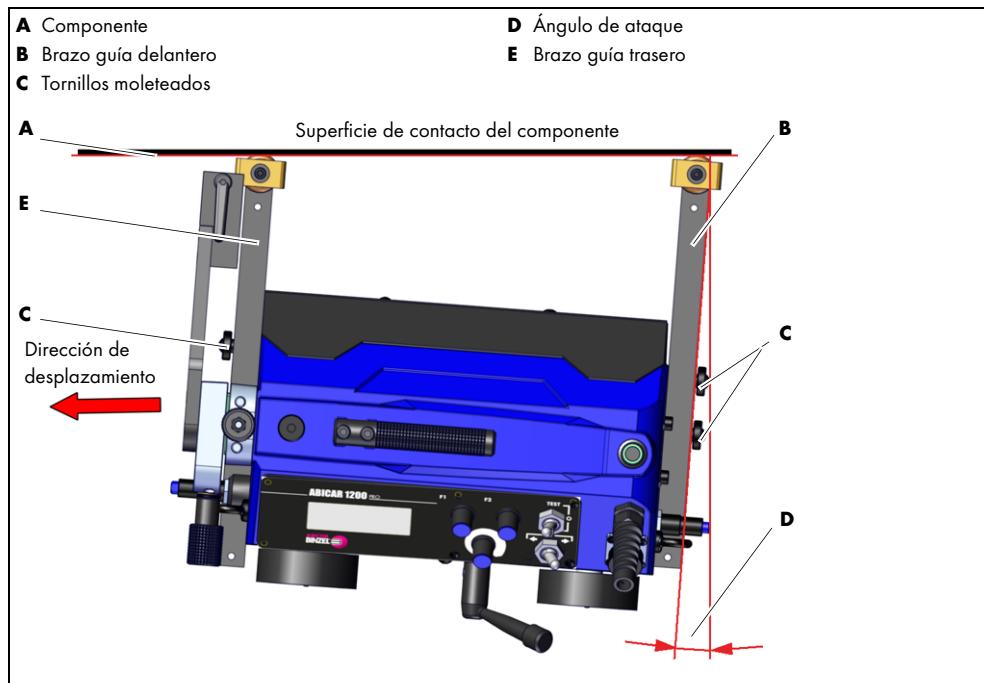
Ajuste de la antorcha de soldadura
